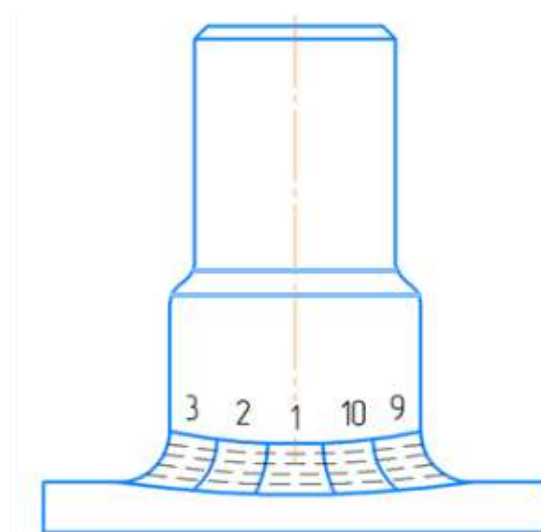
Контролируемый элемент коллектора пара: 1-10 – участки сварного шва
